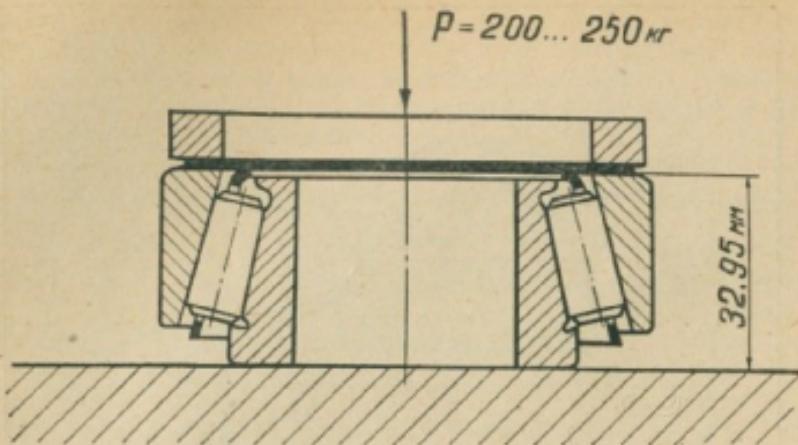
Замер монтажной высоты подшипника ведущей шестерни главной передачи
